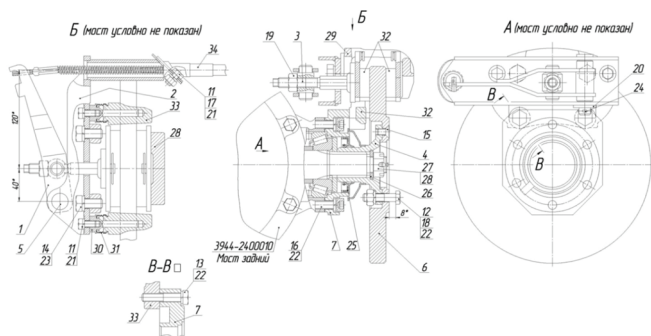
Стояночный тормоз дискового типа.
